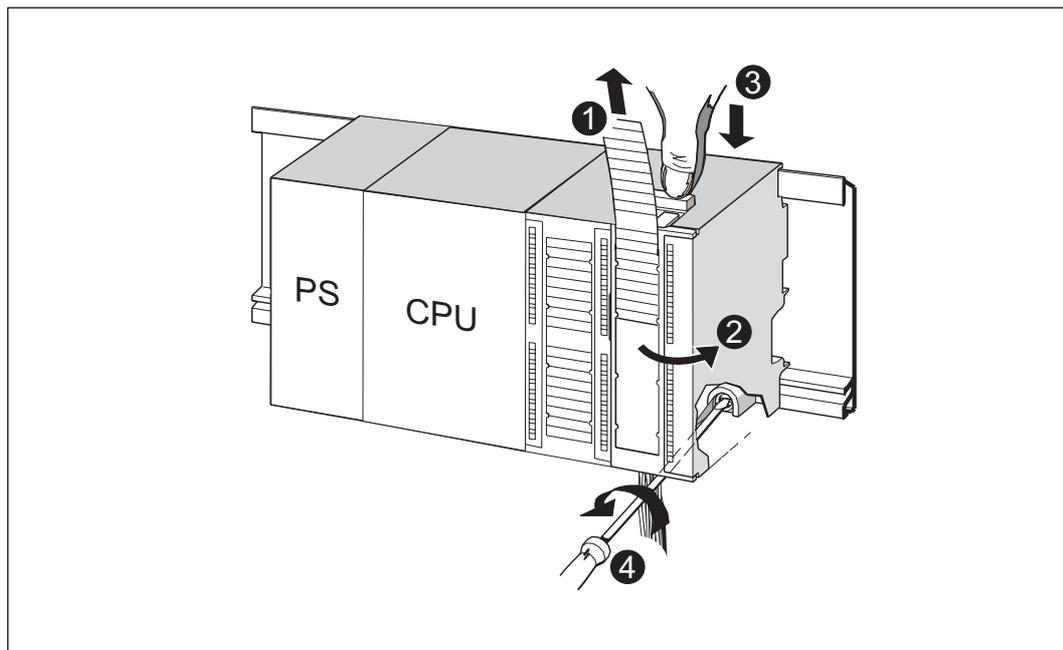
Sbloccaggio del connettore frontale e smontaggio dell'unità
